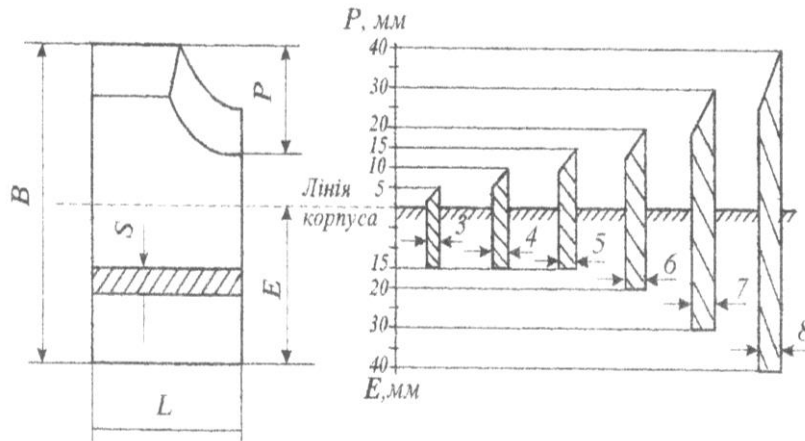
Схема залежності між лінійними параметрами сталевого ножа
